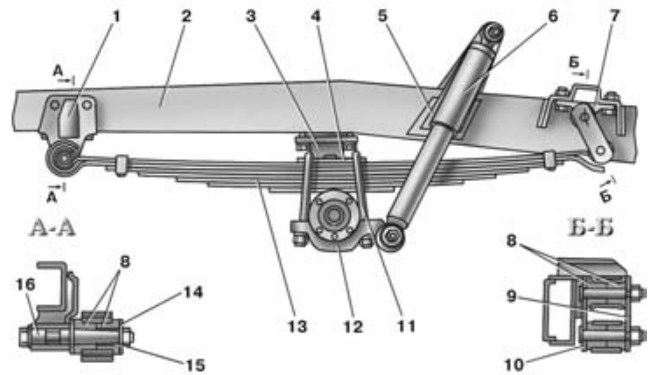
Передняя подвеска автомобилей семейства УАЗ-31512: 1 - передний кронштейн; 2 - рама; 3 - буфер; 4 - накладка; 5 - кронштейн амортизатора; 6 - амортизатор; 7 - задний кронштейн; 8 - резиновые втулки; 9 - наружная щека серьги; 10 - внутренняя щека серьги; 11 - стремянка; 12 - подкладка; 13 - рессора; 14 - шайба; 15 - втулка рессоры; 16 - ось рессоры.
